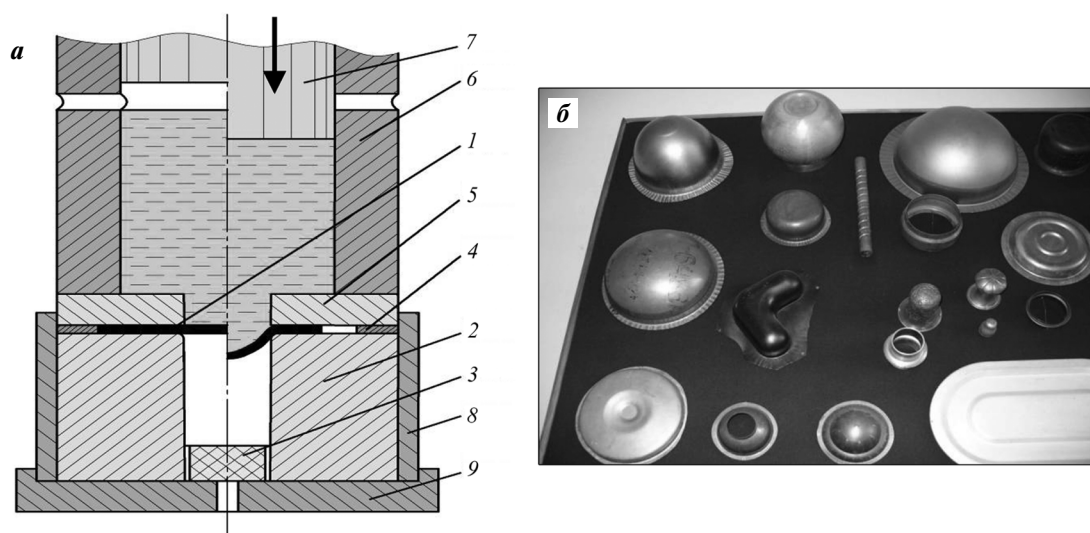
Схема гидроударной штамповки через жидкую среду (*а*) и примеры получаемых изделий из листового металла (*б*)
